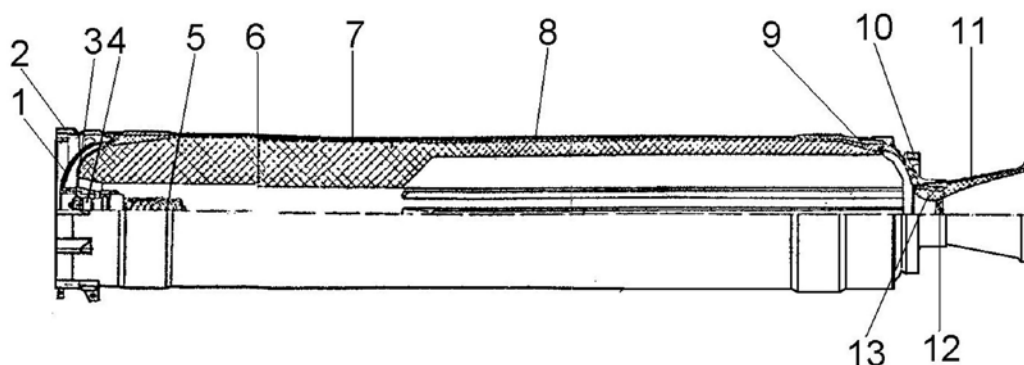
Двигатель ракеты: 1 – днище переднее с теплозащитной чашей; 2 – силовой шпангоут; 3 – сигнализатор давления; 4 – пиропатроны; 5 – воспламенитель; 6 – заряд твердого топлива; 7 – корпус; 8 – теплозащитное покрытие; 9 – днище заднее с теплозащитной чашей; 10 – посадочный пояс; 11 – сопловой блок; 12 – заглушка; 13 – вкладыш
